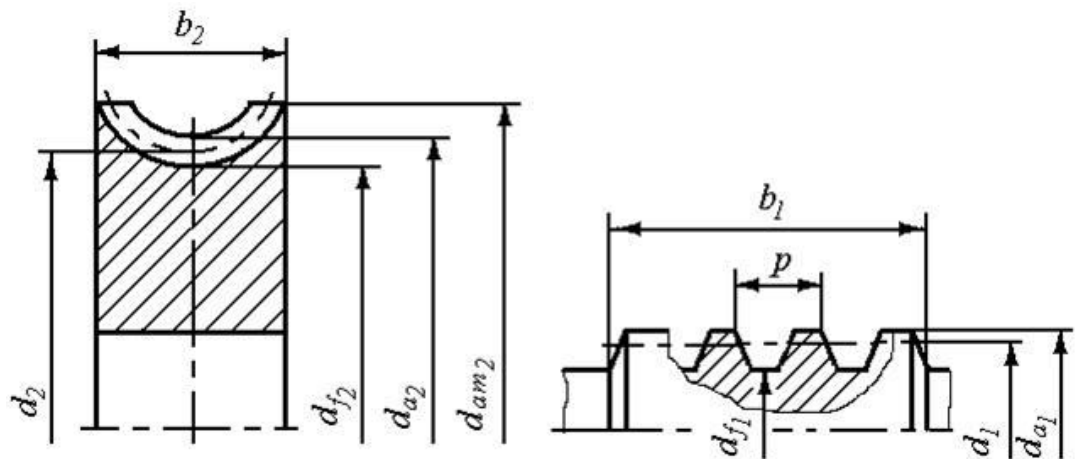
Геометричні параметри черв'ячного колеса і черв'яка:
